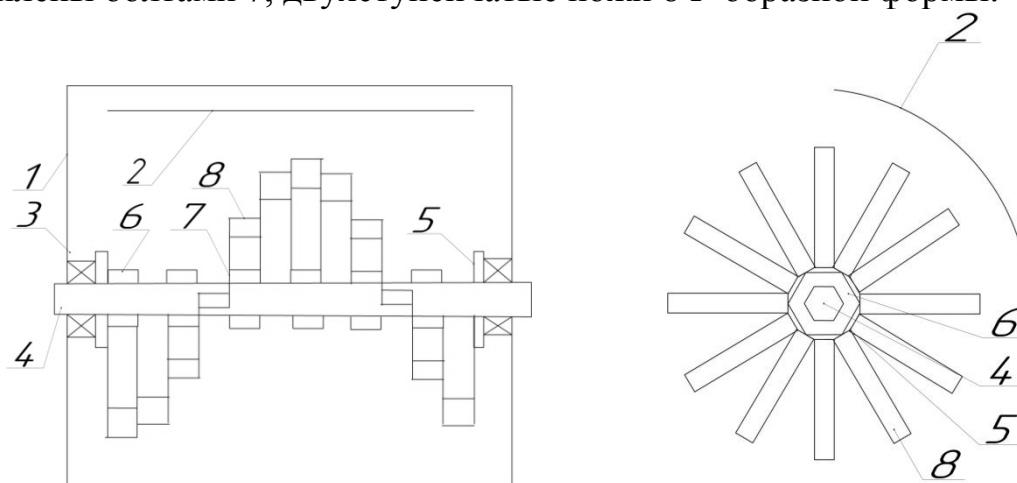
Почвообрабатывающая фреза с двухступенчатыми ножами F-образной формы
